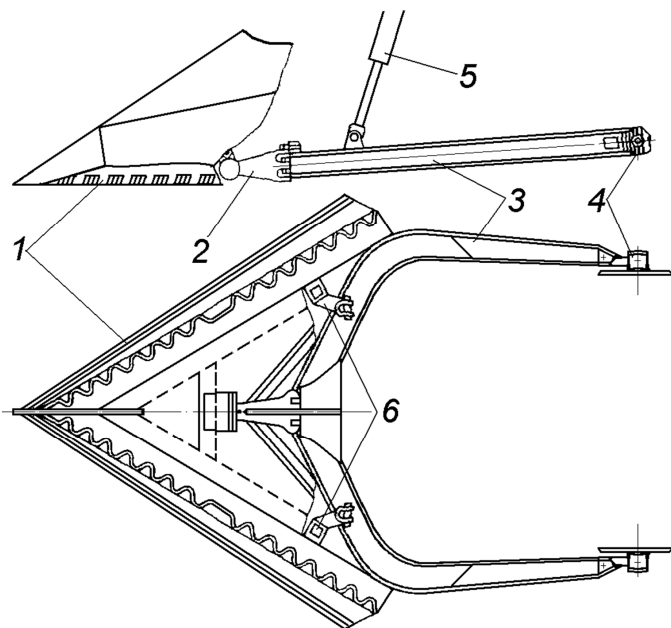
Рабочее оборудование кустореза: 1 – клиновидный кусторезный отвал; 2 – цапфа центрального сферического шарнира; 3 – универсальная толкающая рама; 4 – упругие шарниры; 5 – гидроцилиндры подъёма и опускания отвала; 6 – амортизационное устройство.
